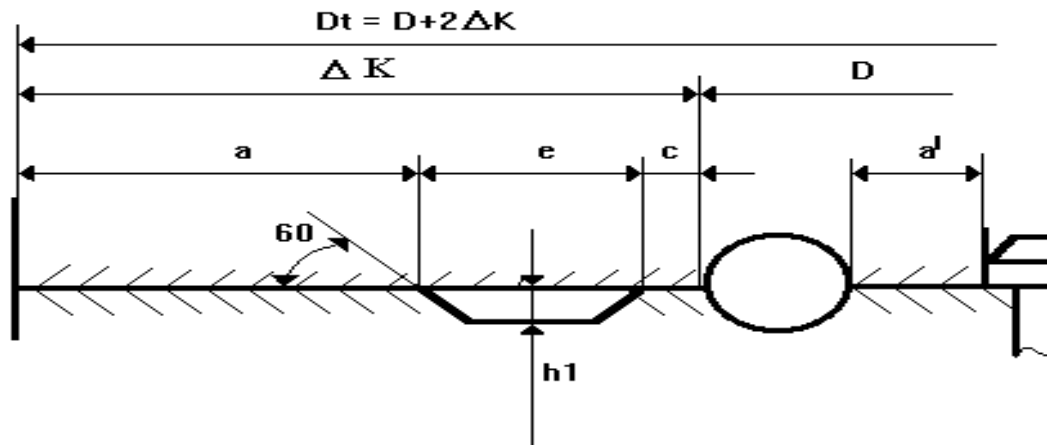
Dimensiones de la cavidad para el sobrante de material.
